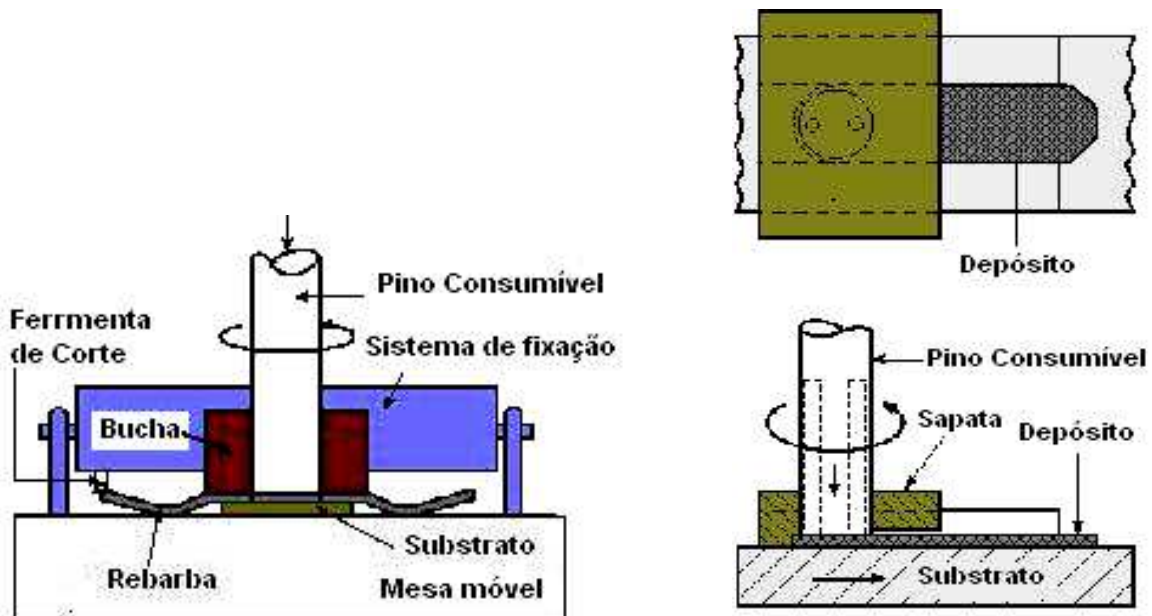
Dispositivos testados para restrição da rebarba (adaptado de ANDREWS 2007).
